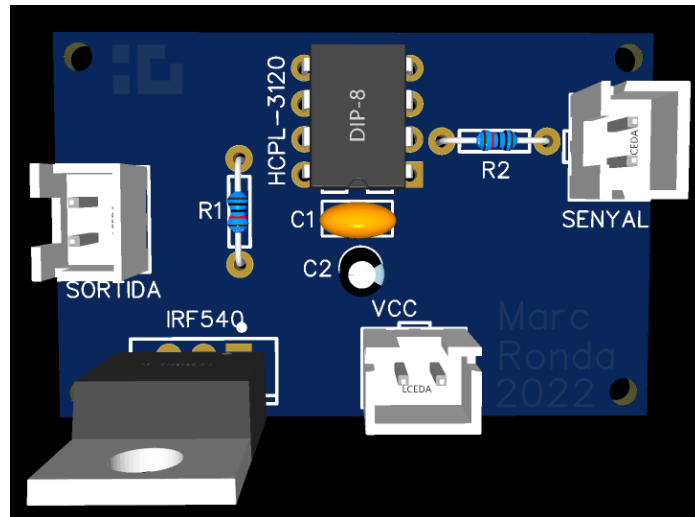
Disseny en 3D de la PCB (Disseny 5) (Font: Pròpia)
